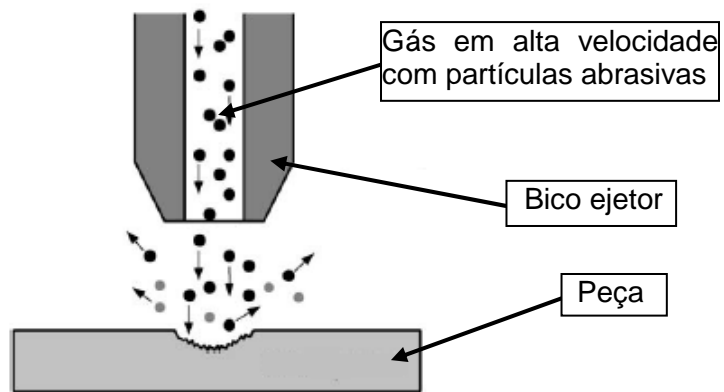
Princípio do processo de Usinagem por Jato Abrasivo (BENEDICT, 1987).
